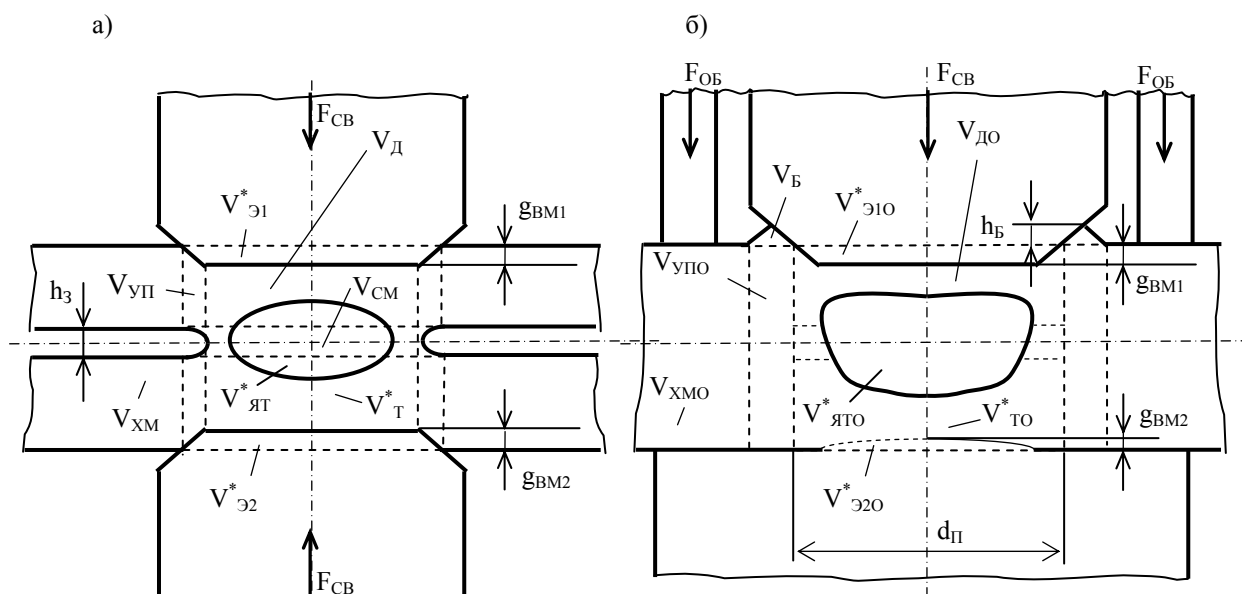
Схема зоны формирования соединения: а – при двухсторонней точечной сварке; б – при сварке с обжатием периферийной зоны
